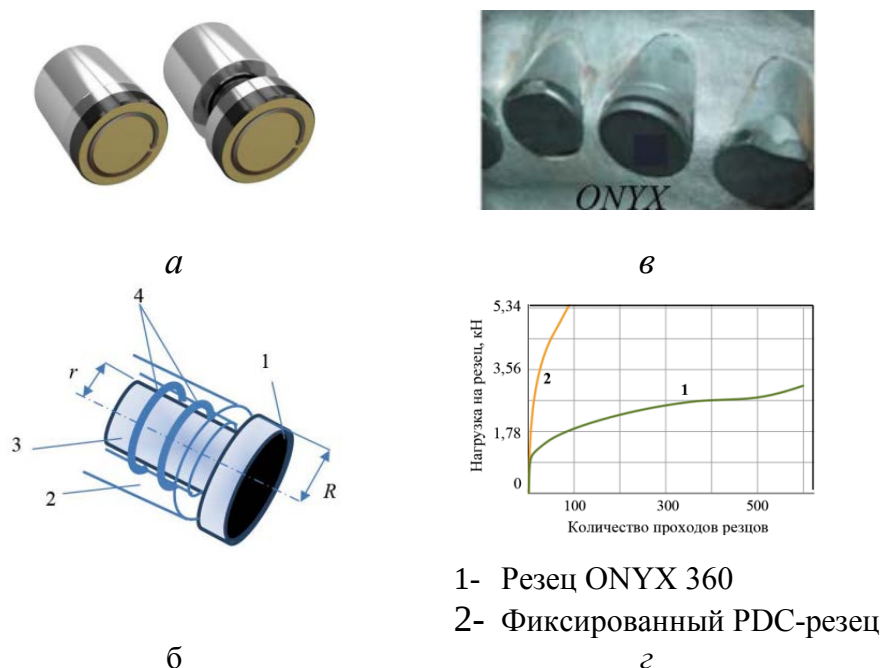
Алмазные резцы ONYX 360, обеспечивающие равномерный износ режущей части долот и высокий ресурс инструмента: *а* – общий вид вращающегося резца; *б* - конструкция вращающегося PDC-резца: 1 – PDC-резец; 2 – корпус; 3 – ось; 4 – стопорные упругие кольца ONYX 360; *в*, *г* – сравнительный износ и ресурс фиксированного и вращающегося PDC-резцов.
